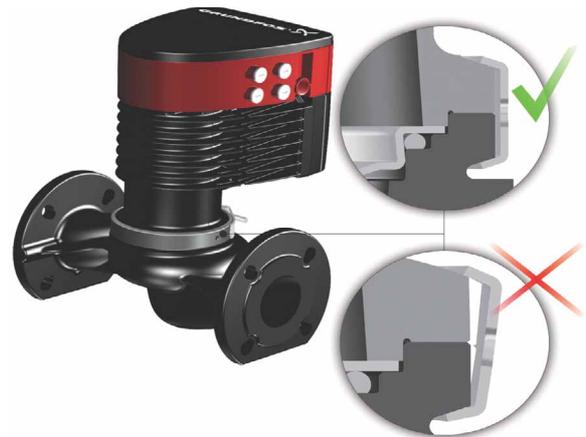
Montieren des Pumpenkopfes auf dem Pumpengehäuse
